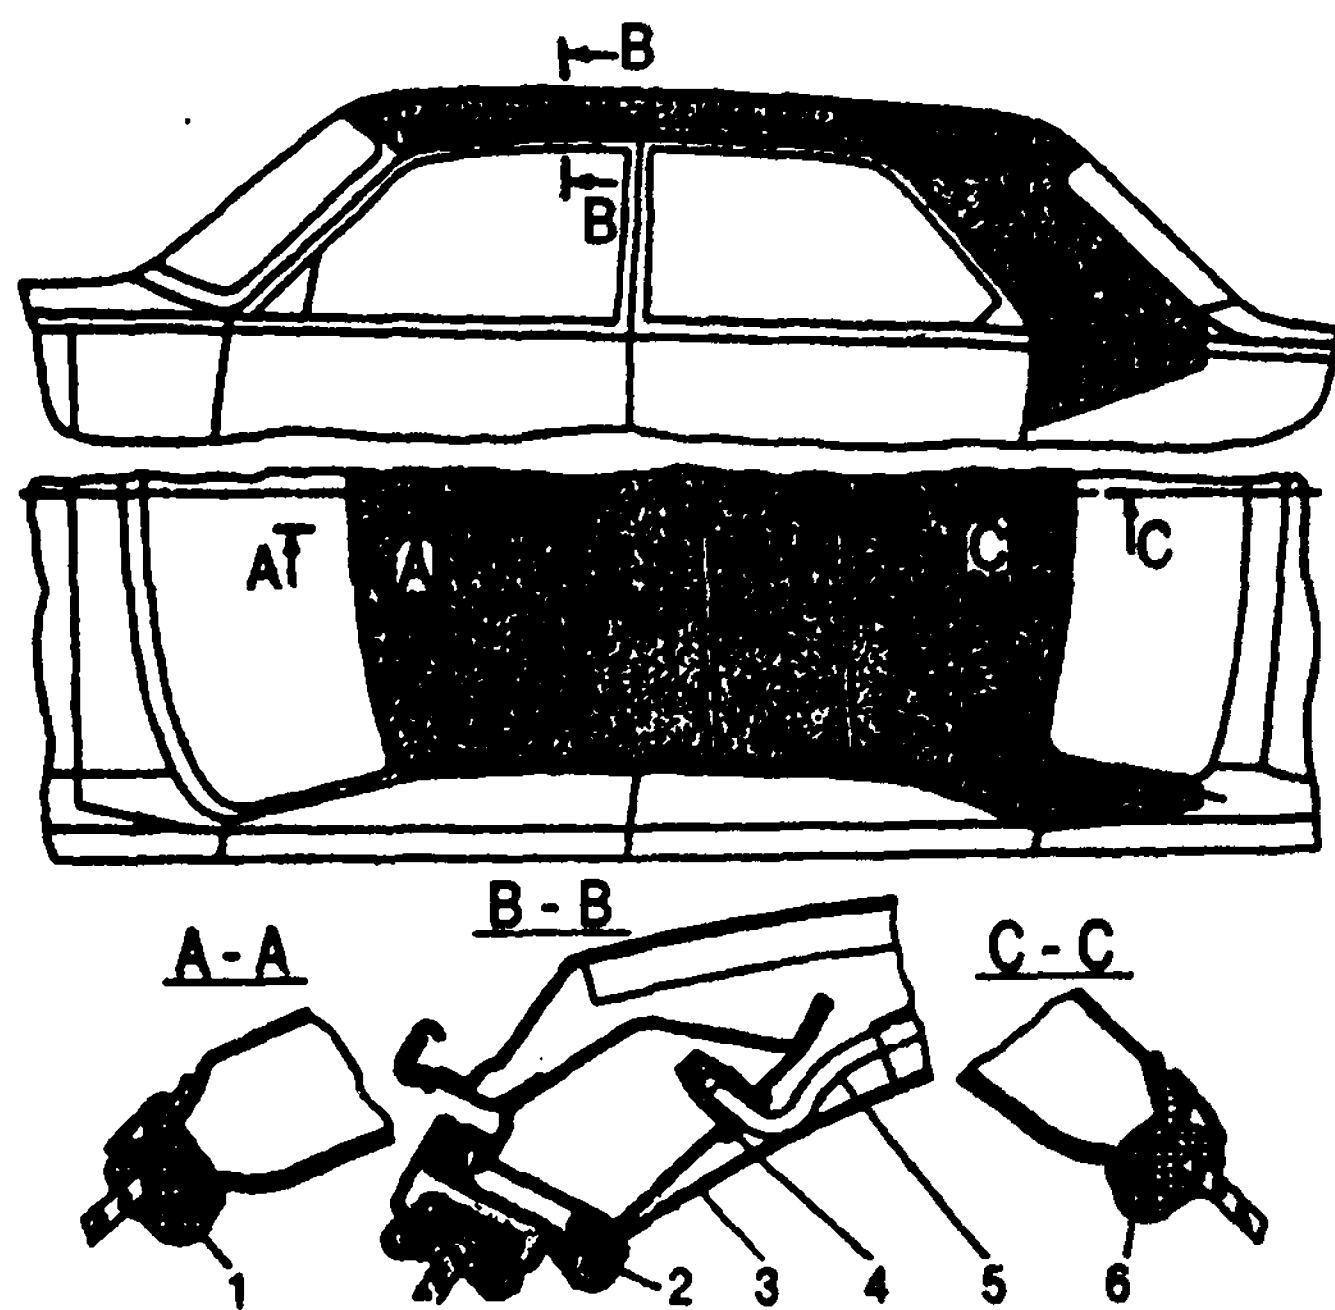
Установка обивки крыши: 1 - уплотнитель ветрового стекла; 2 - кант проема двери; 3 - обивка крыши; 4 - втулка дуги; 5 - дуга обивки; 6 - уплотнитель окна задка
